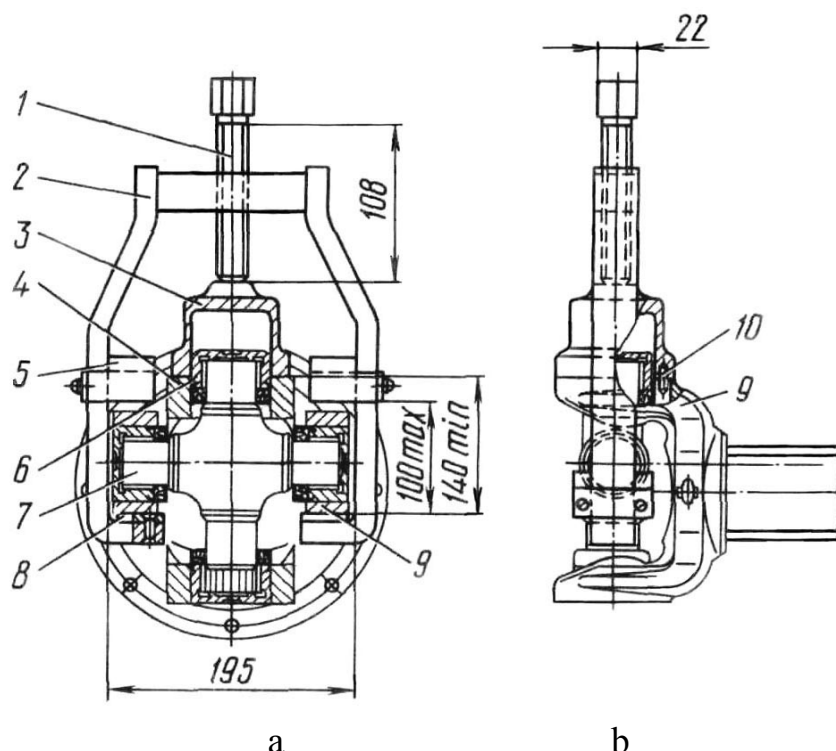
Выпрессовка подшипников крестовины карданного вала:
